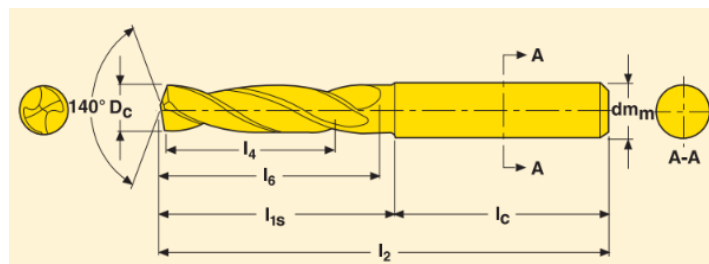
Свердло SD1103-0500-020-06R1 [14, с.25]
